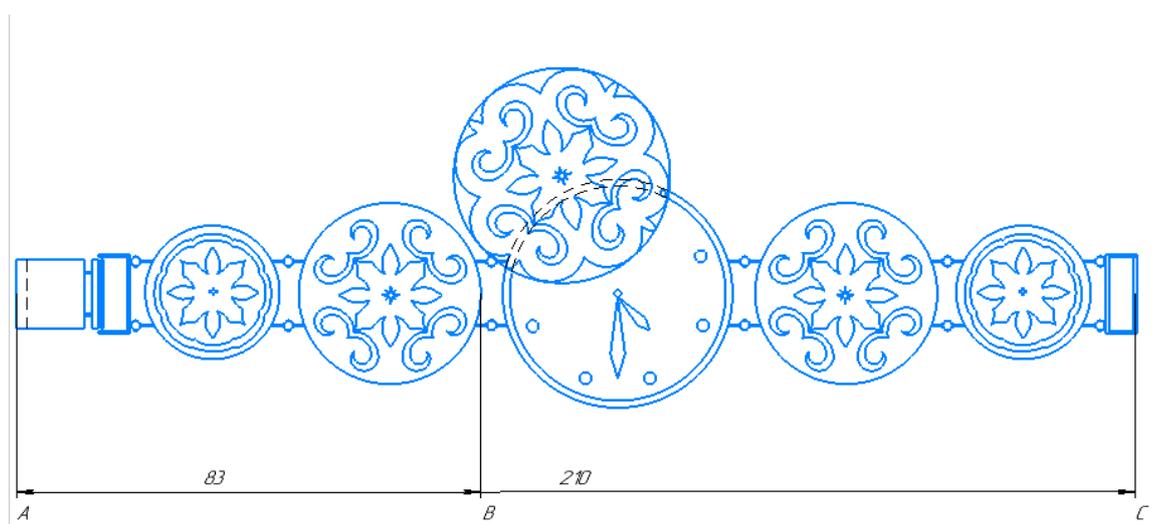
Чертеж эскиза для определения золотого сечения
